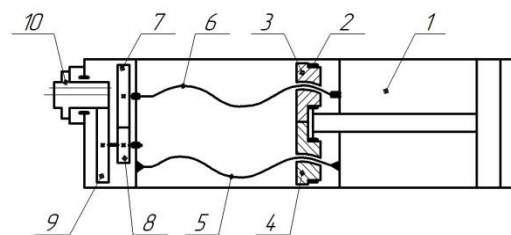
Компоновка резбонарезного станка с комбинированным МПС
